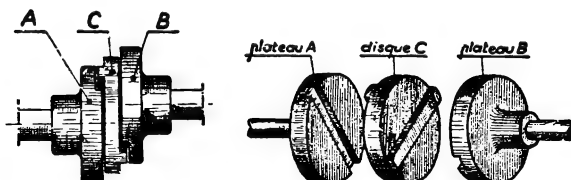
Ensemble et pièces séparées d'un joint d'Oldham.
